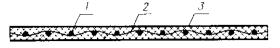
Кордшнуровой прорезиненный ремень
